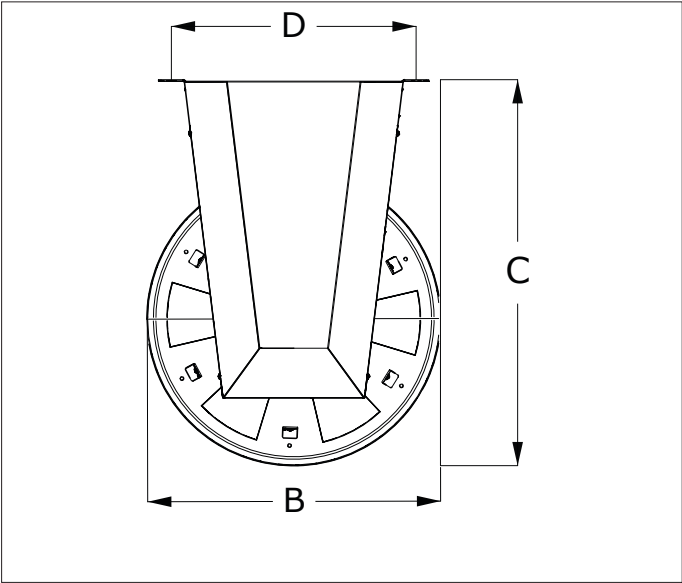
Seitliche Ansicht des Schlauchaufrollers
